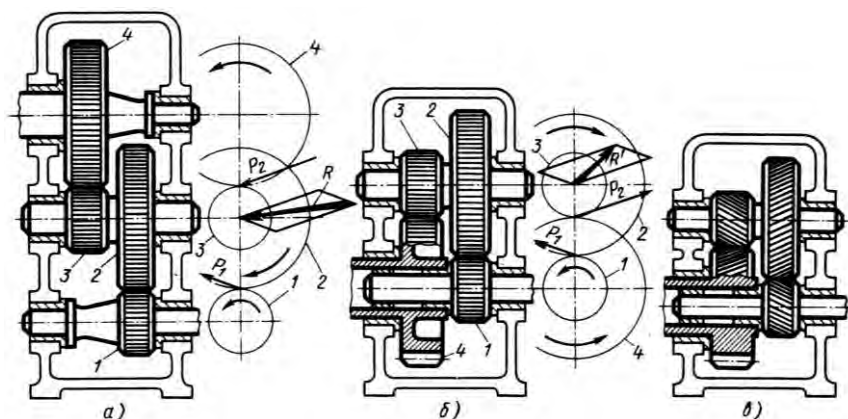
Уменьшение габаритных размеров и массы двухступенчатого редуктора
